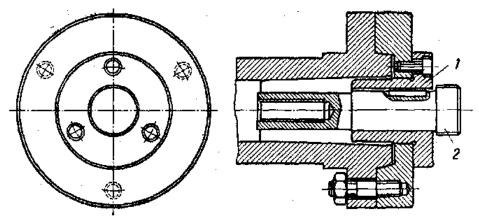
Оправка с механизированным приводом для установки по резьбе
